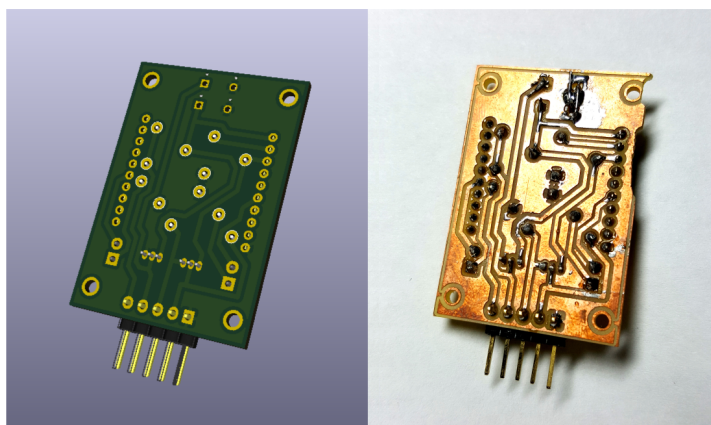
PCB 3D vs PCB DiY (reverso)
